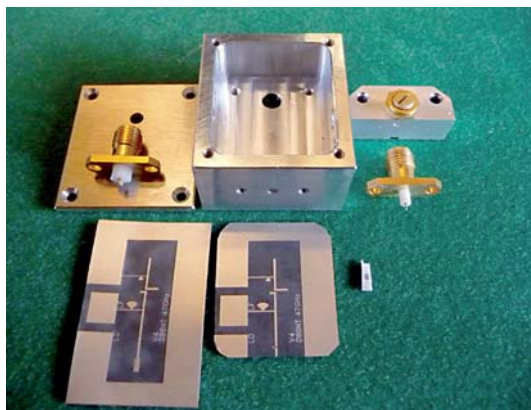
Gehäuse für koaxiale Einspeisung mit original PCB Nr. 48 und eingepasster PCB mit Koppel-C 0,5 pF
